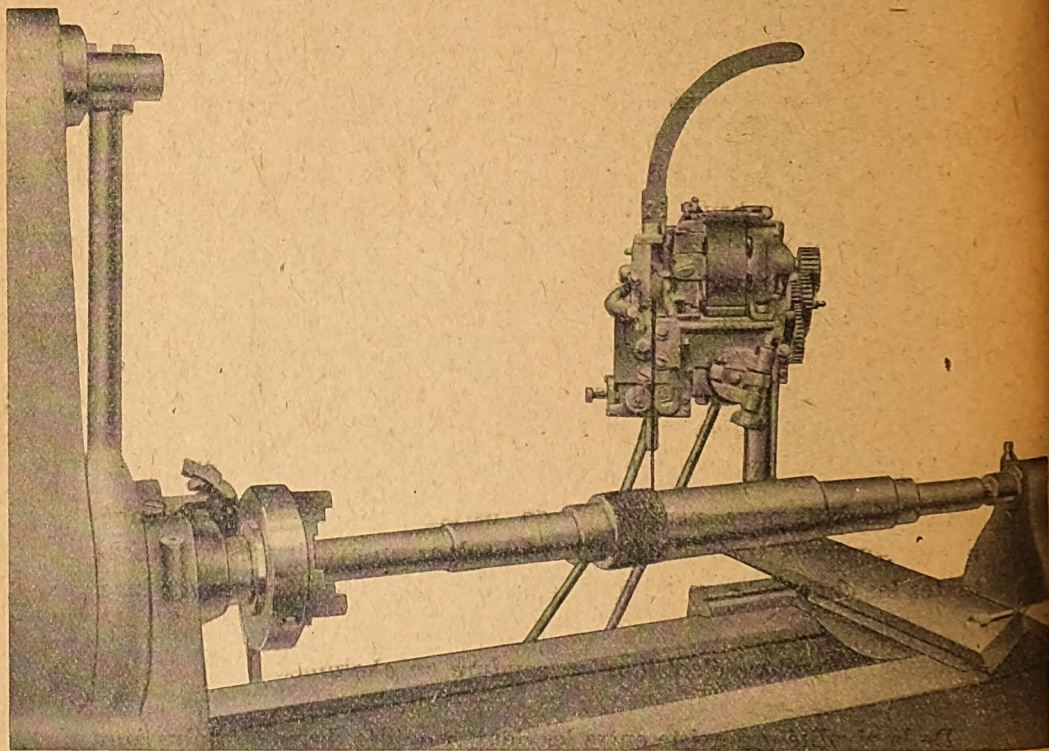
Vue d'une machine de soudure automatique G. E. C. rechargeant un arbre de moteur électrique usé.
